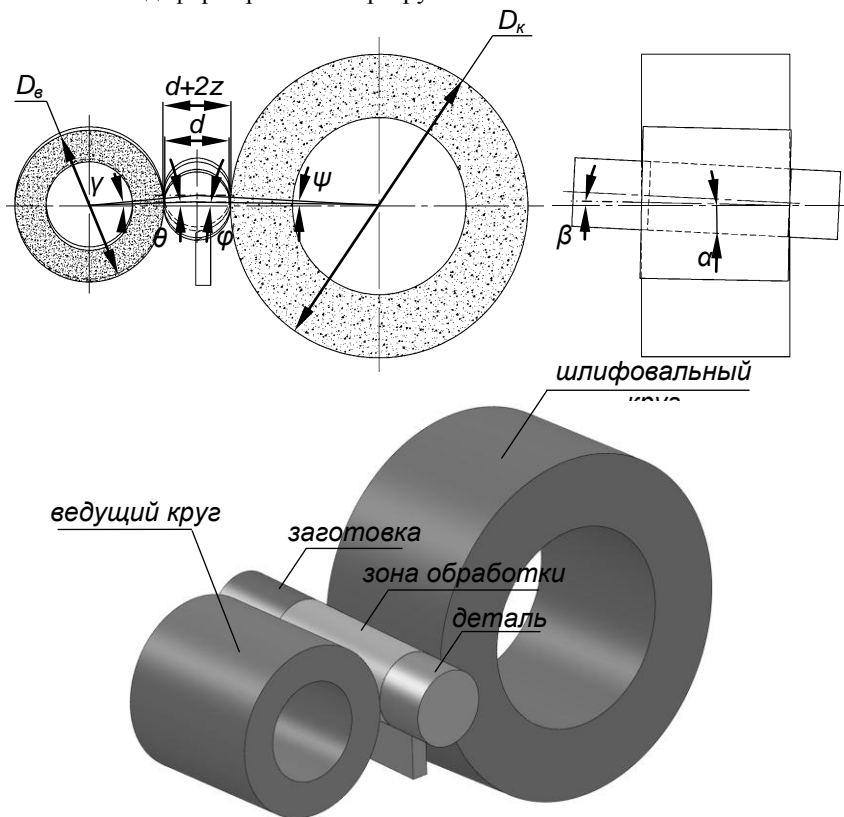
Схема бесцентрового шлифования со скрещивающимися осями инструмента и детали
